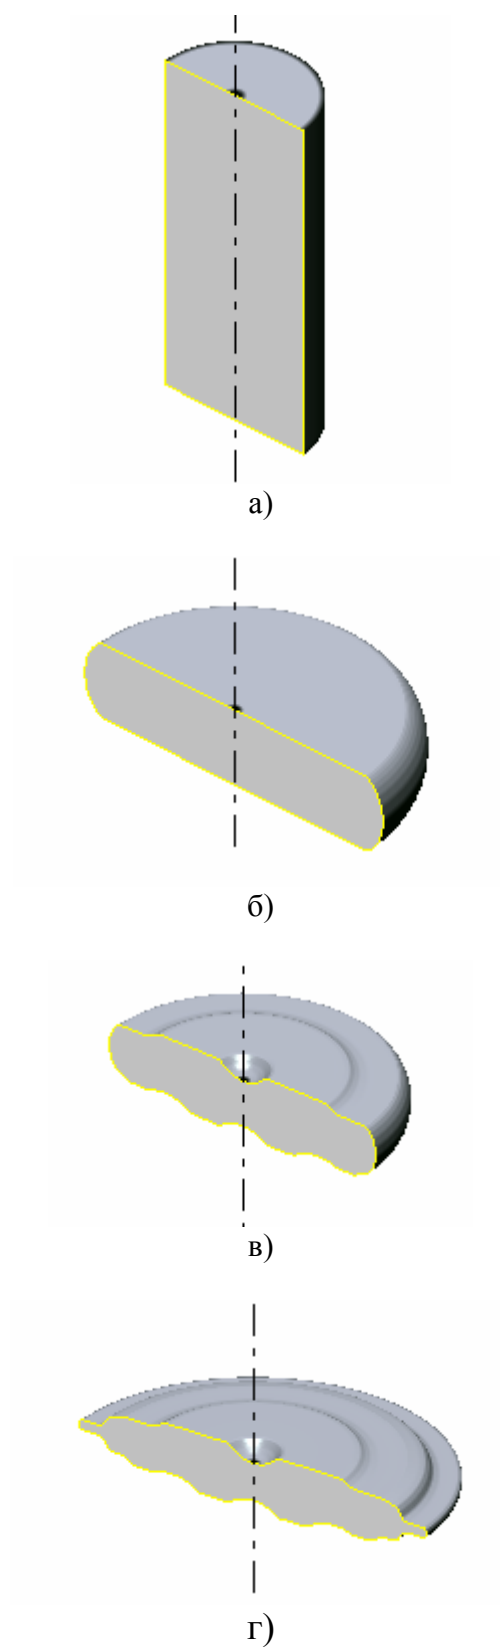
Технологические переходы штамповки заготовки диска из сплава ЭП 742-ИД с окончательной штамповкой в открытом штампе: а) исходная заготовка $\phi 260 \times 580$ мм, б) осадка, в) штамповка в предварительном ручье, г) штамповка в окончательном ручье
